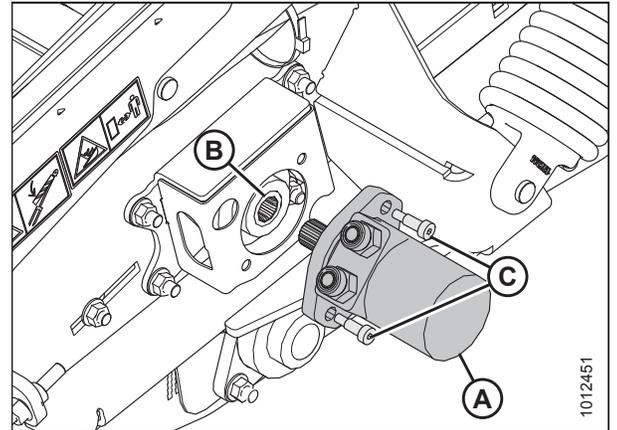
Motor hidráulico frontal – lado esquerdo
